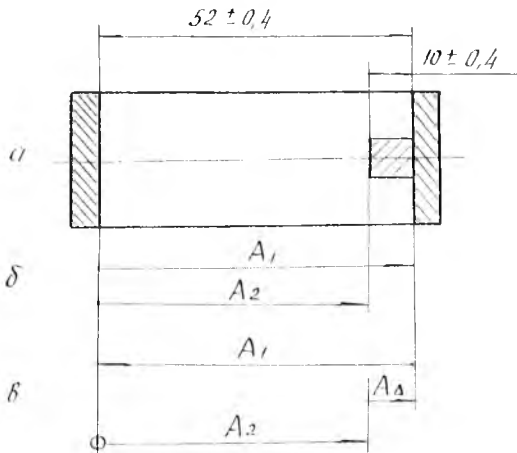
Эскиз детали (а), размерная схема ТП (б) и размерная цепь (в)
